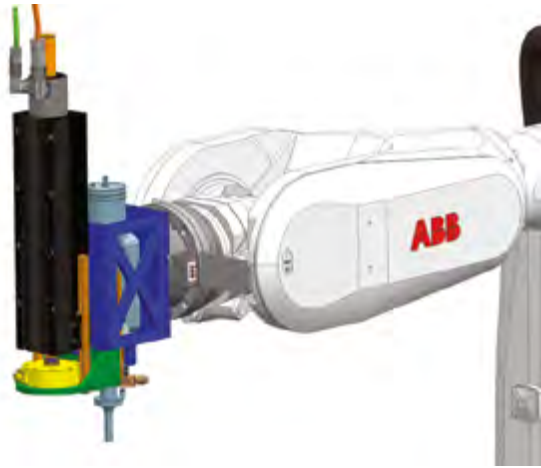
Ultraschall-Schweisswerkzeug
